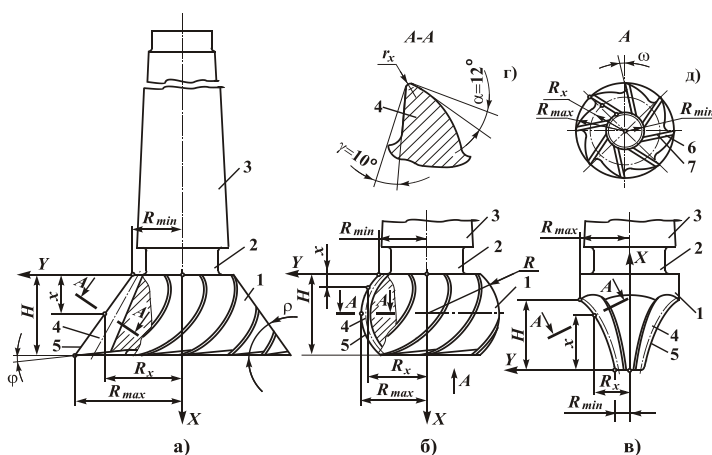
Схеми кінцевих фрез з різними варіантами ріжучої частини
